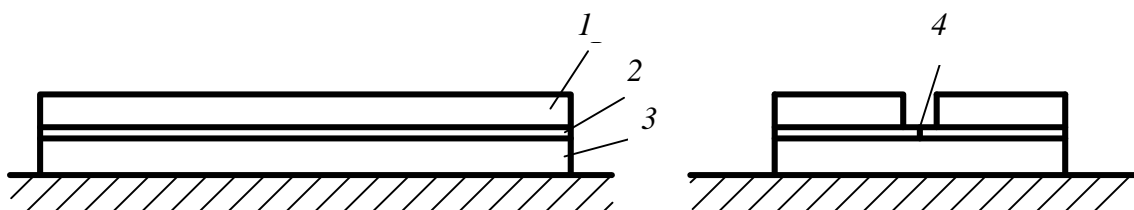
Схема фиксации образцов: 1 – стальная пластина; 2 – образец из алюминия; 3 – подложка; 4 – стык
